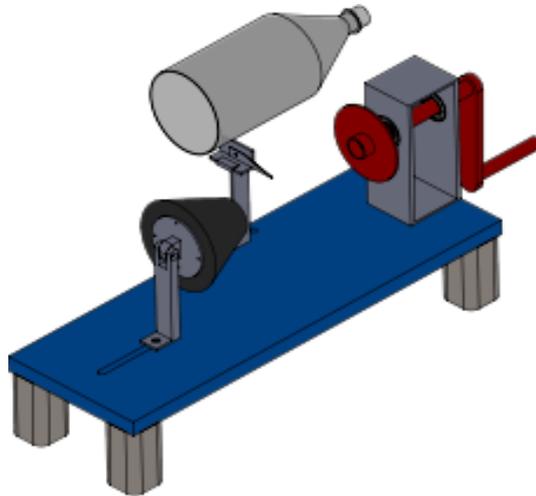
Modelo máquina seccionadora de embudo de botellas
